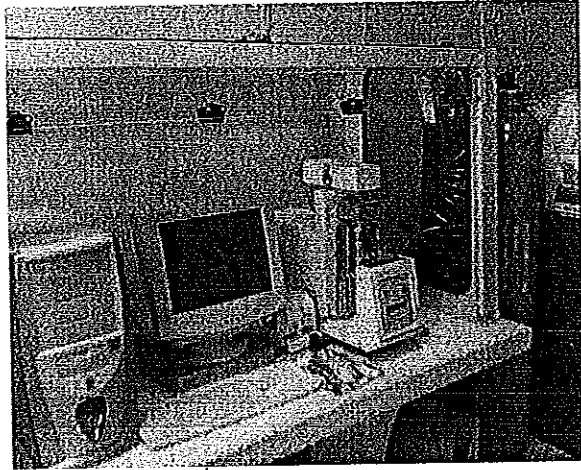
เครื่องฉีดเทอร์โมพลาสติก (Plastic Injection Moulding Machine)
